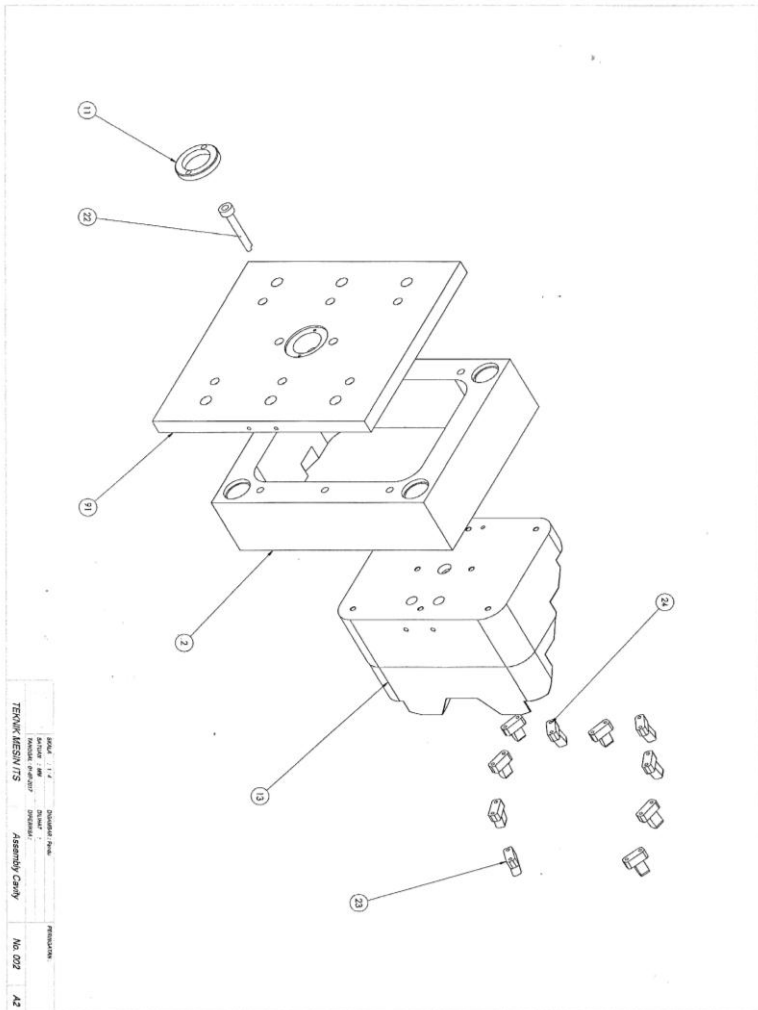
Detail *drawing assembly mold* mika lampu sein
